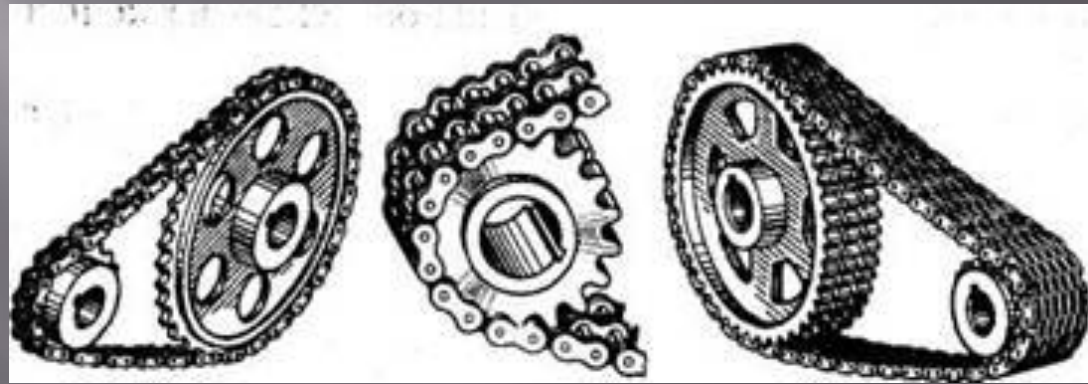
Цепная передача: 1 — ведущая звездочка; 2 — ведомая звездочка; 3 — цепь; 4 — натяжное устройство
